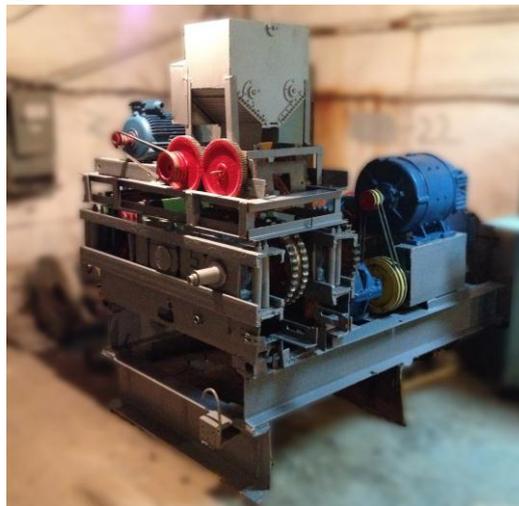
Пресс – валковый агрегат с устройствами для предварительного уплотнения шихты
